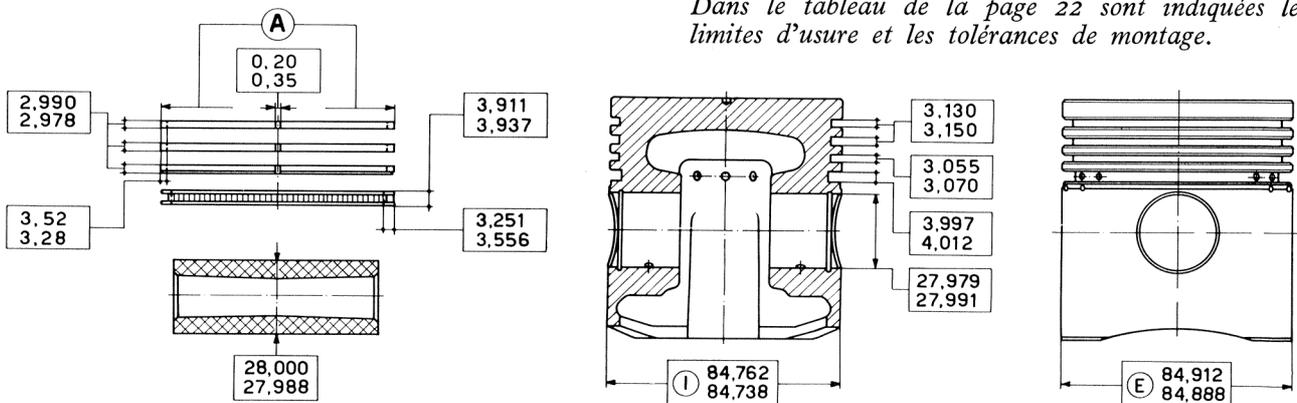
Dimensions normales des pistons des segments et des axes.
